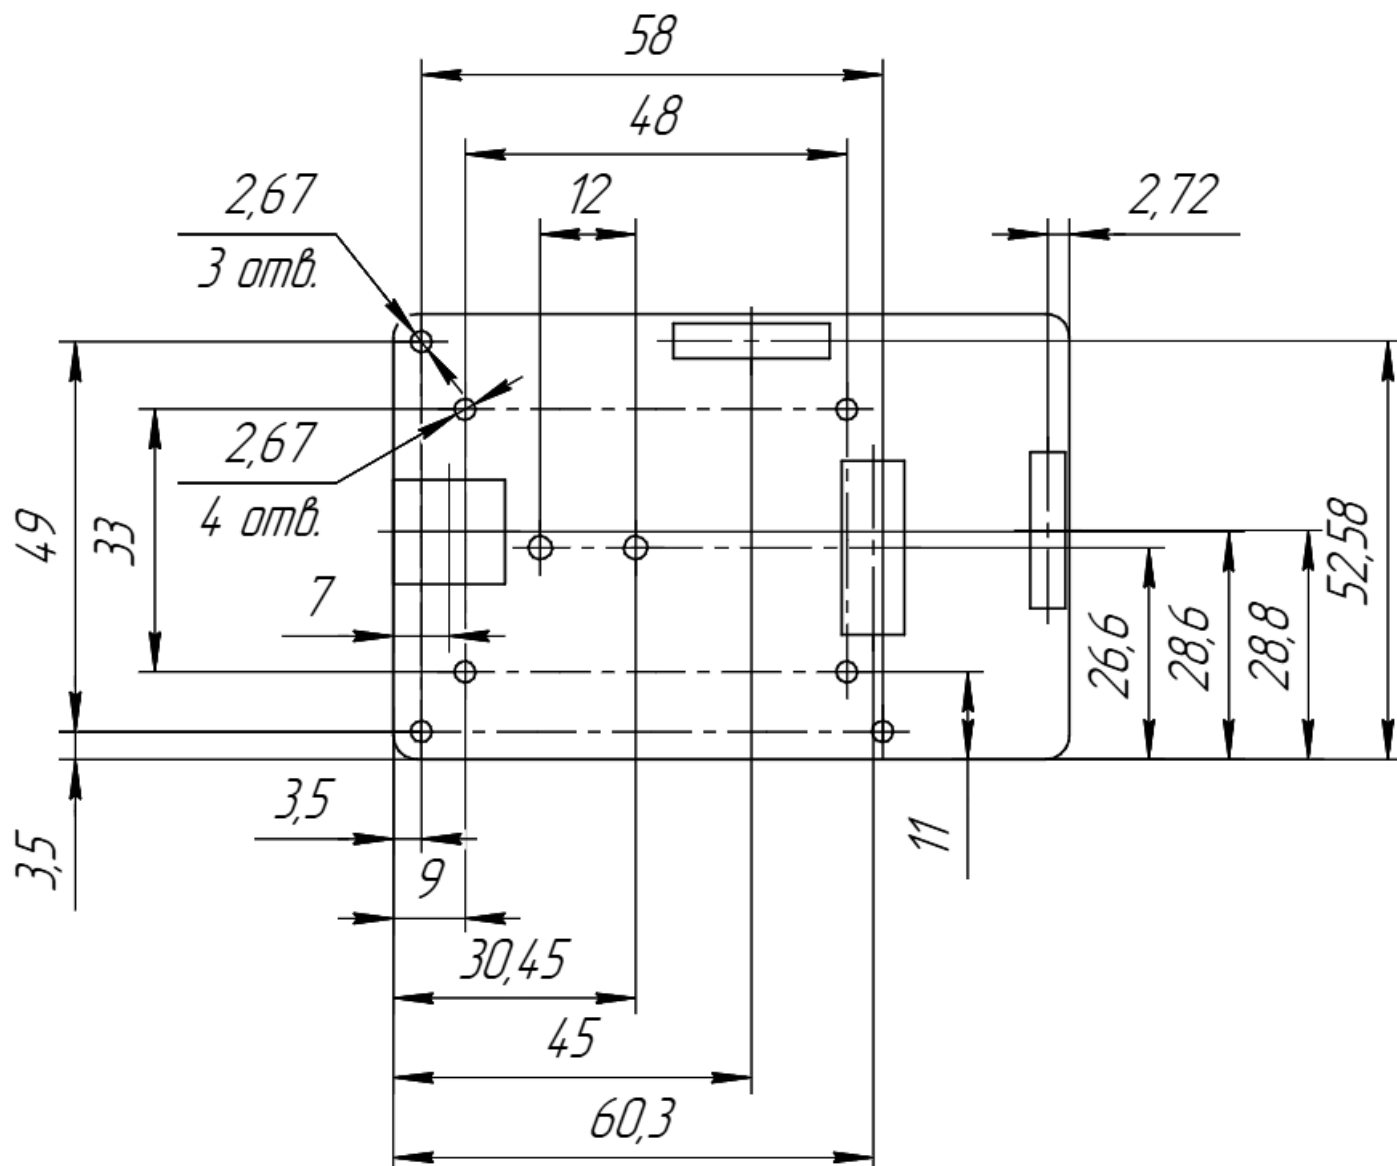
Чертеж ELTAY RM66, вид снизу.
